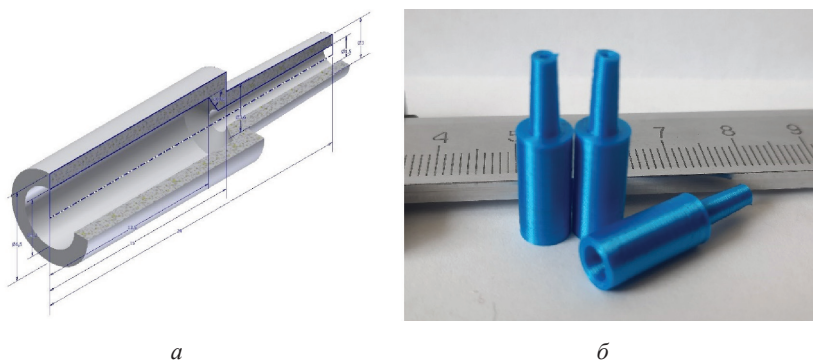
Твердотельная 3D-модель с размерами (а) и опытный образец (б) переходной канюли для иглы Куликовского и шприца однократного применения типа «Луер»
